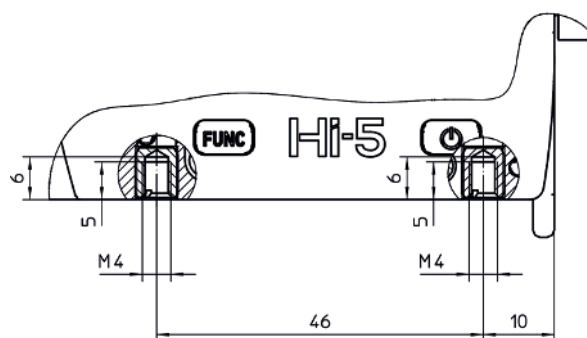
Detalhe da vista frontal Hi-5 Y
